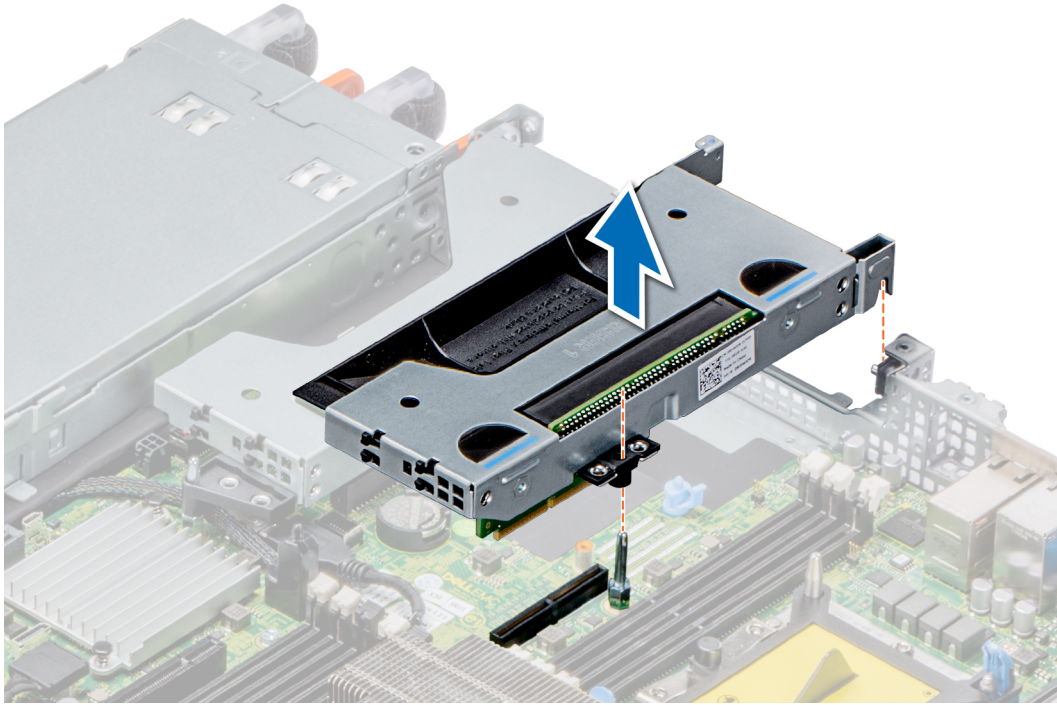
Extracción del soporte vertical derecho de perfil bajo (soporte vertical 1)
